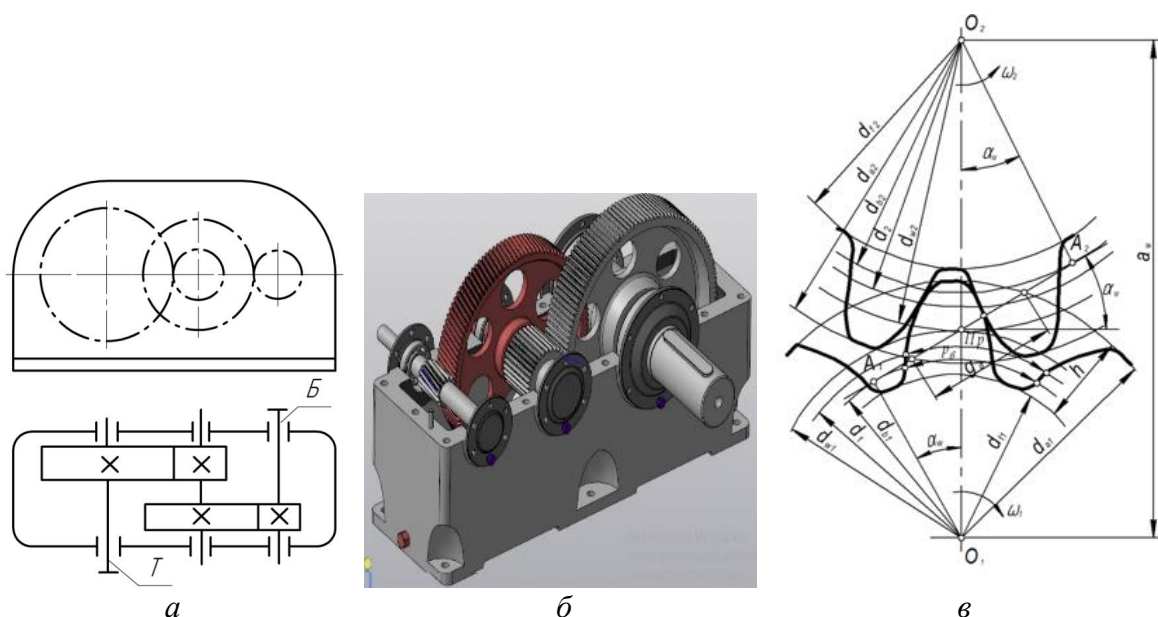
Редуктор цилиндрический зубчатый: *а* – кинематическая схема, *б* – вид со снятой крышкой, *в* – зацепление колес в передаче
